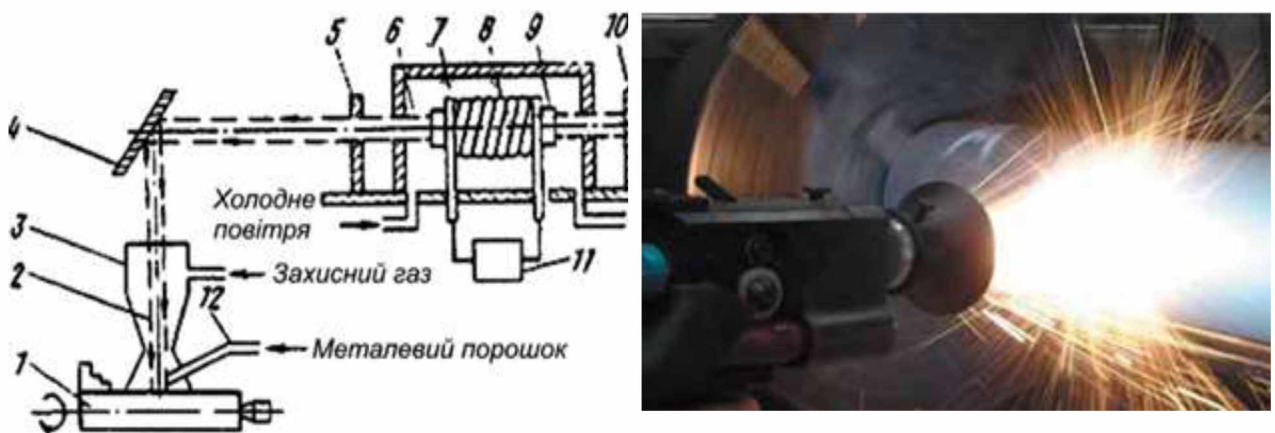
Схема установки для лазерного наплавлення [13].
